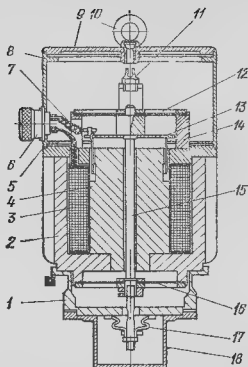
Электромеханический преобразователь (ЭМП): 1 — крышка нижняя; 2 — корпус; 3 — обмотка подмагничивания; 4 — сердечник; 5 — выводы обмотки подмагничивания; 6 — штексельный разъем; 7 — выводы динамической катушки; 8 — кожух; 9 — крышка; 10 — пш болт; 11 — пружинный установщик индикатора часового типа; 12 и 16 — плоские центрующие пружины; 13 — динамическая катушка; 14 — обойма; 15 — шток; 17 — уплотняющий сальфон; 18 — предохранительный стакан (на период транспортировки)
